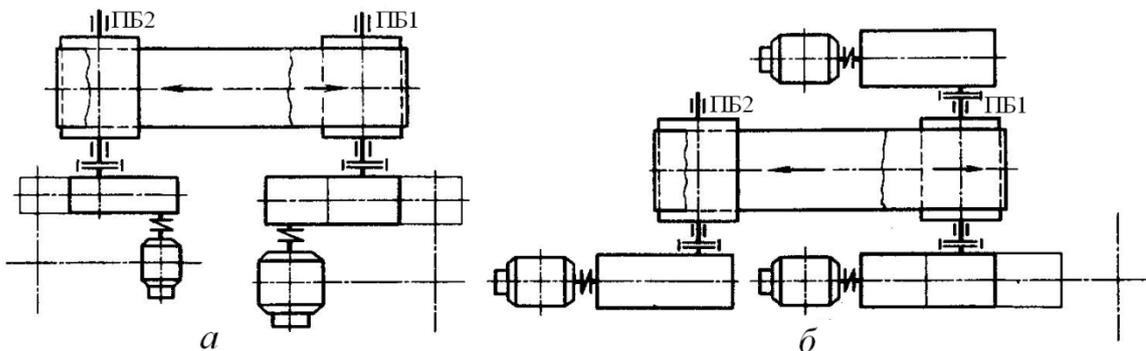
Схемы двухбарабанного привода: *а* – с двумя двигателями, *б* – с тремя двигателями
